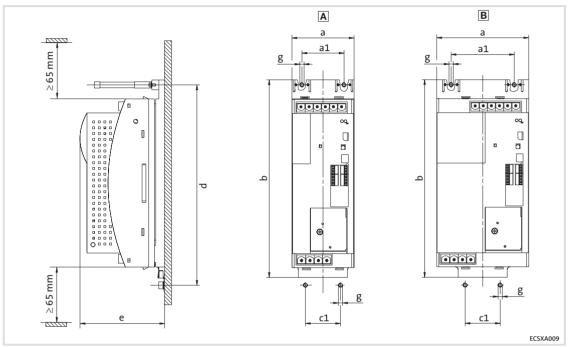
Dimensioni per il montaggio con tecnica "Cold-Plate"
